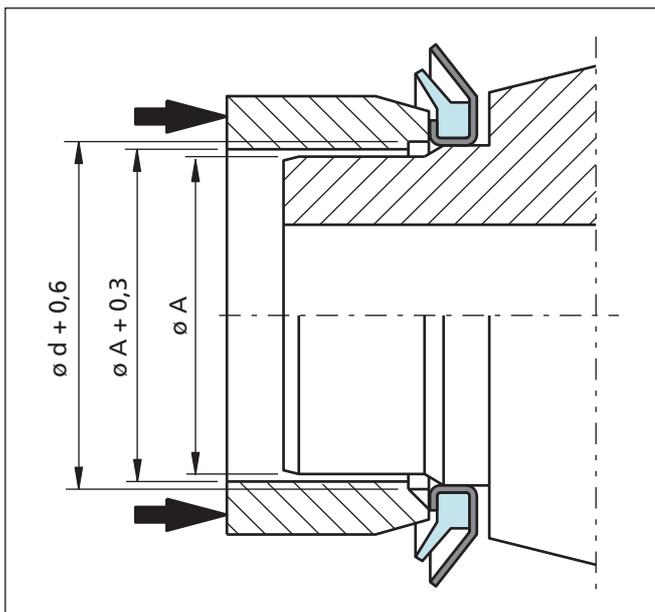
Montagewerkzeug. Bei der Montage gegen einen Ansatz darf die Montagekraft nicht zu groß sein, damit das Gehäuse des GAMMA-Ringes nicht beschädigt wird.
